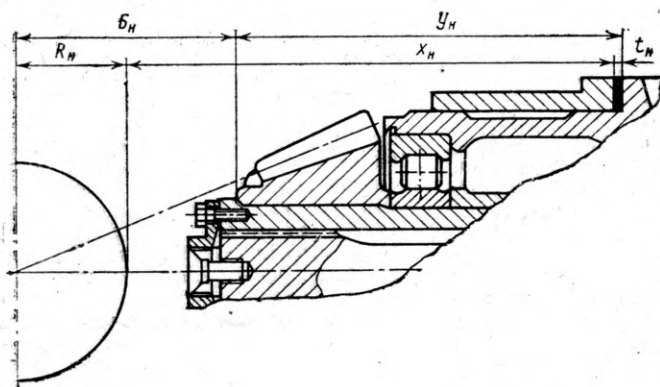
Измерение размеров для нижнего коленчатого вала: $Б_n$ — размер от торца шестерни до вершины конуса зубьев; $У_n$ — расстояние от торца шестерни до привалочной плоскости корпуса вертикальной передачи (замеряется в цеху до постановки в блок); $Х_n$ — расстояние от посадочной плоскости в блоке дизеля до шейки нижнего коленчатого вала; R_n — радиус шейки вала; t_n — толщина регулировочных прокладок
